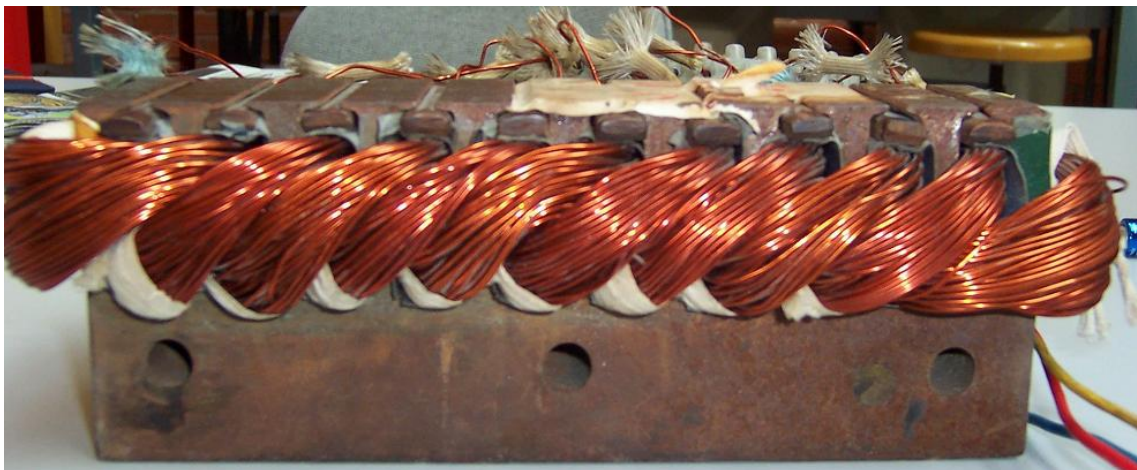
Perfil de la armadura con las cabezas de bobina en primer plano
